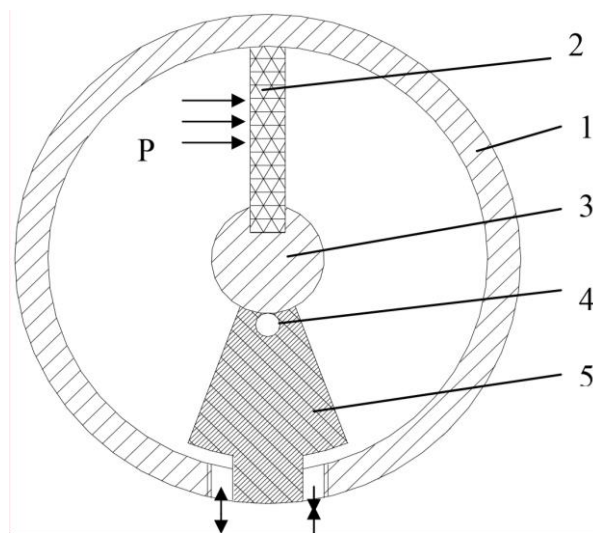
Схема моментного однолопатевого гідроциліндра: 1 - корпус; 2 - пластина; 3 - втулка; 4 - ущільнювальна перемичка; 5 - ущільнювальний елемент.
